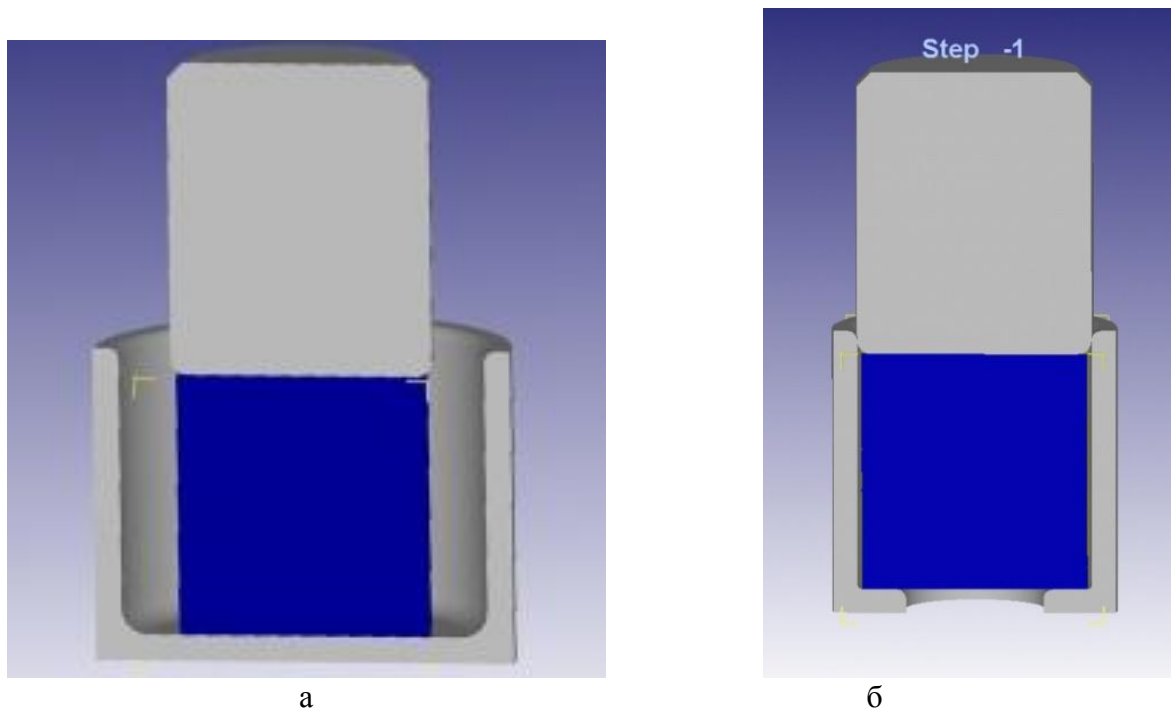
Исходное положение заготовки и рабочего инструмента:
